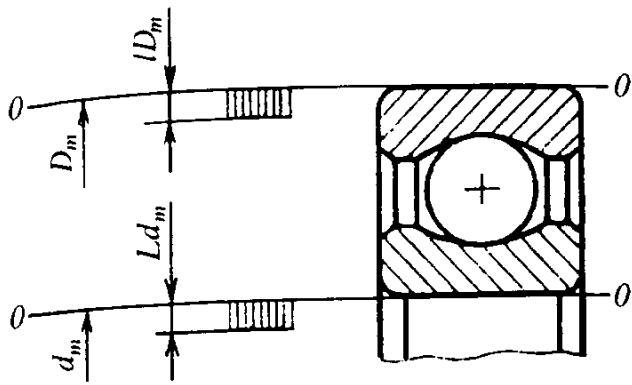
Схема расположения полей допусков на средние наружный диаметр и диаметр отверстия подшипника
